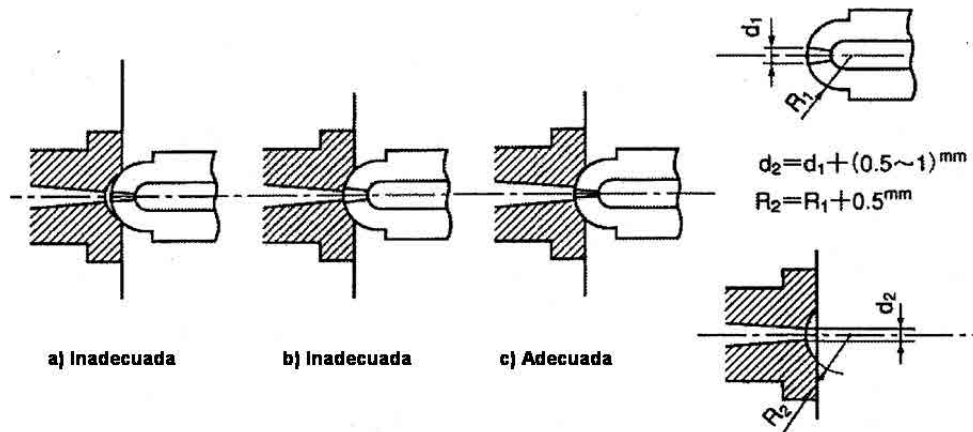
Punto clave para el diseño de puntas de boquilla
